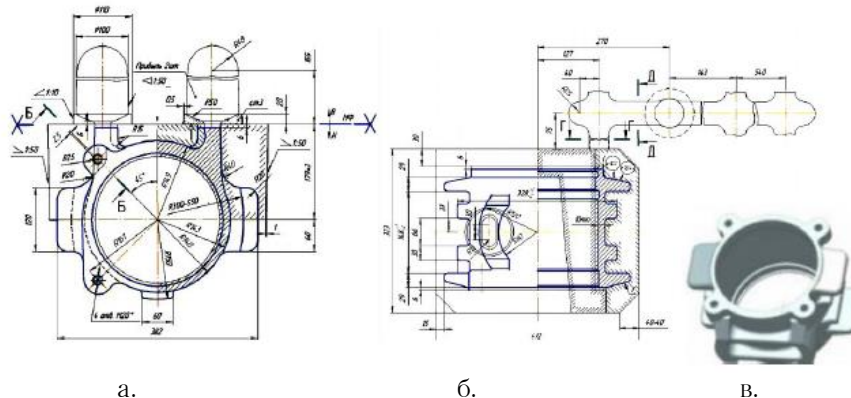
Литая отливка «Корпус буквы»: а. вид сбоку; б. вид сверху; в. общий вид
